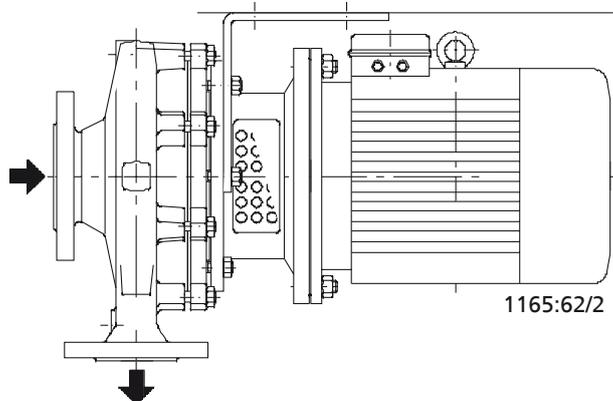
Fijación del pie de bomba arriba, hasta el tamaño de motor 112 = 4 kW
